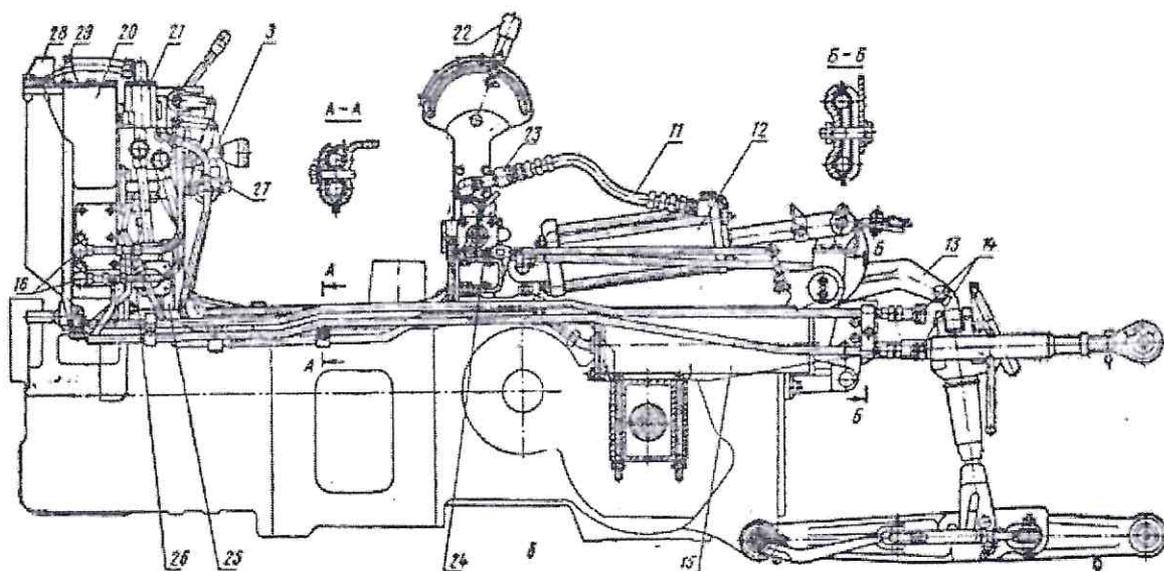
Схема гидравлики вид слева МТЗ 80
